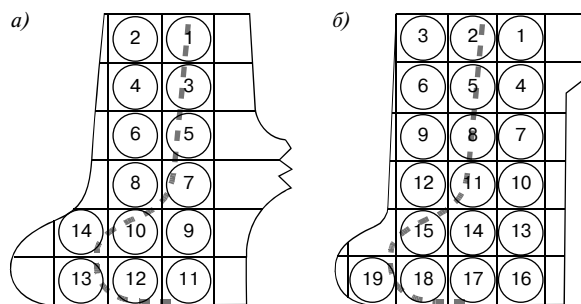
Направления вырезки образцов из цельнокатаного колеса (а) и бандажа (б)
